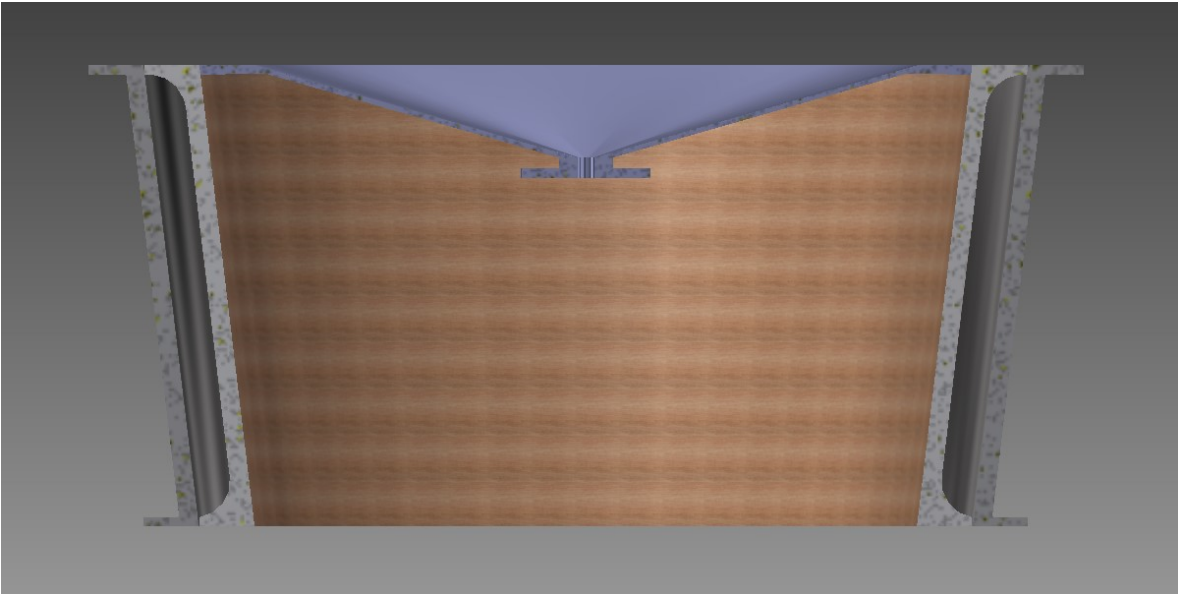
Primera propuesta "corte transversal empaquetamiento para transporte "
